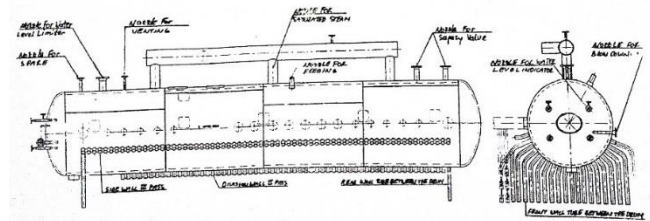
Proses Longseam dan Circume Welding pada Pembuatan Drum
